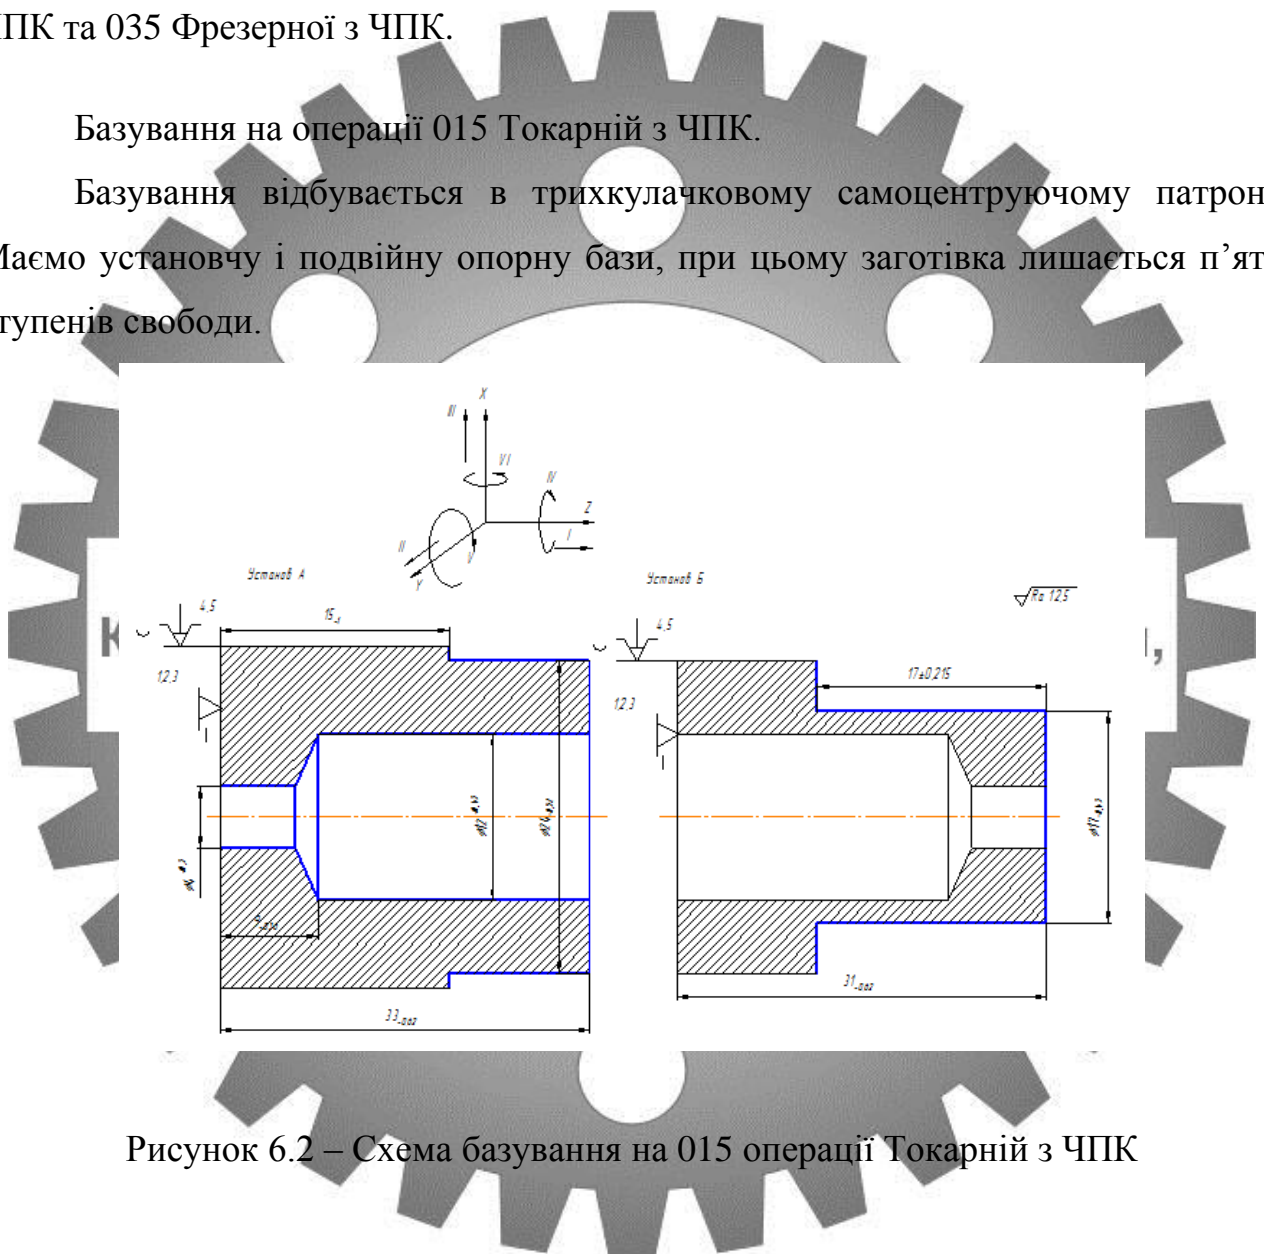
Схема базування на 015 операції Токарній з ЧПК
